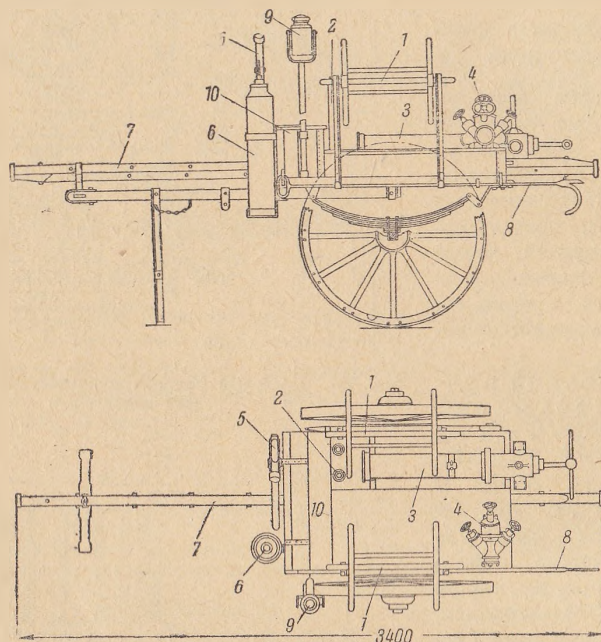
Реквизитный ручной двухколесный рессорный ход.
